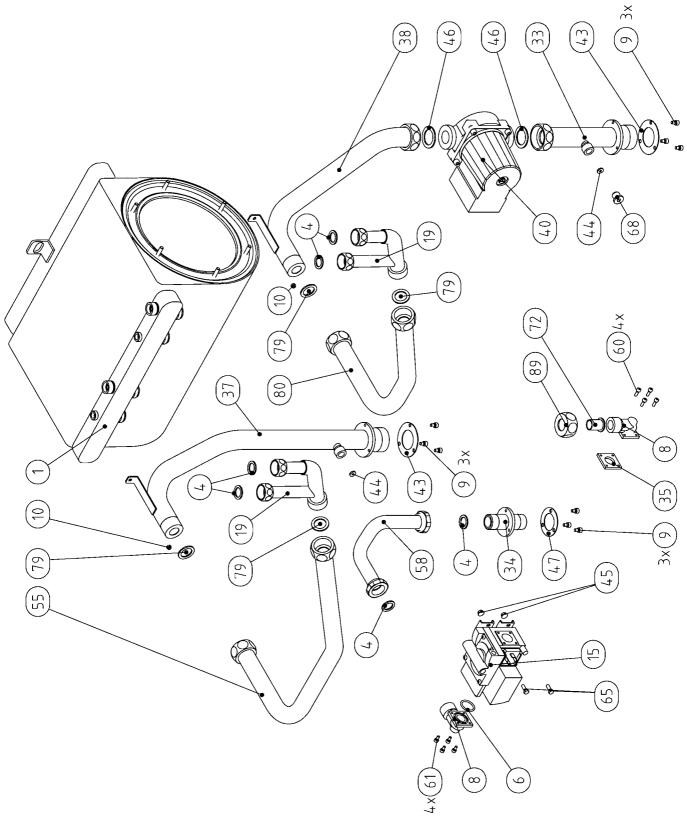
Explosionszeichnung Vor- und Rücklauf
